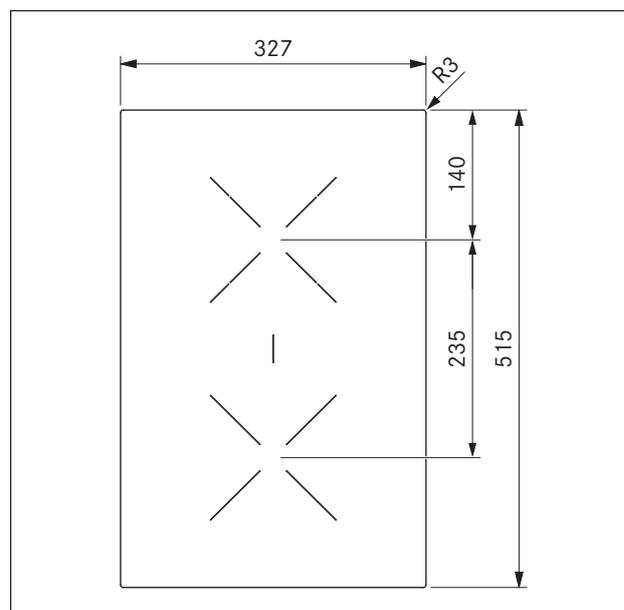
Dimensões do aparelho CKCB, vista de cima
